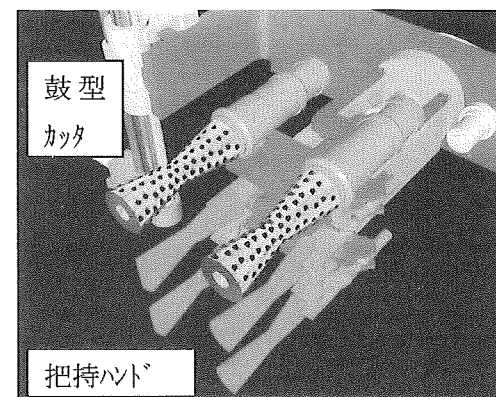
鼓型カッタ切断装置⁵⁾(図-1の丸印部分拡大図)
